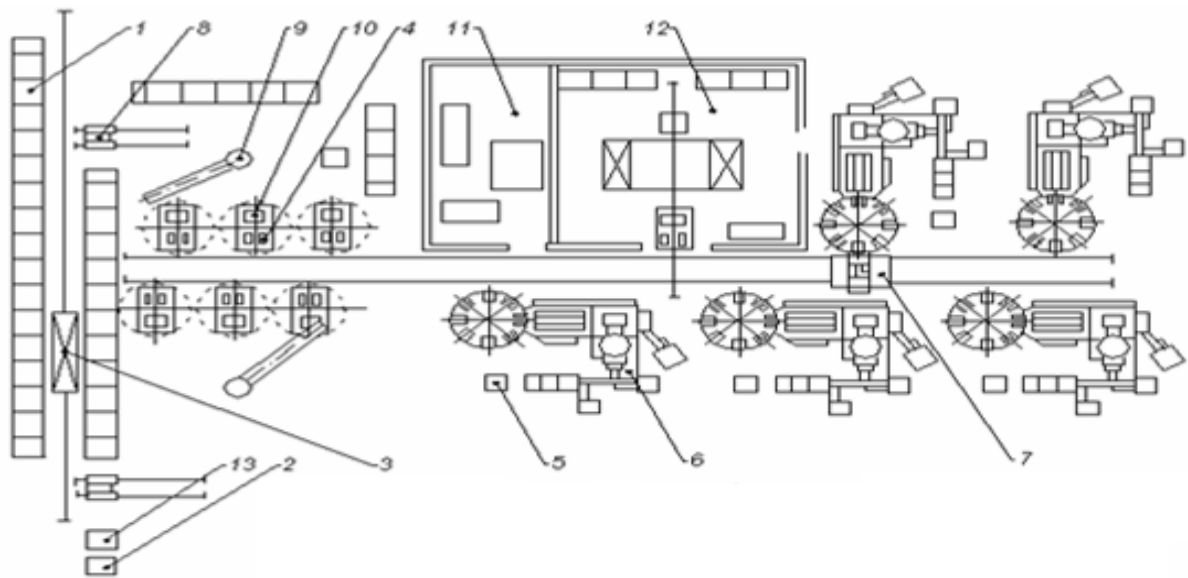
Схема ГВС виробництва корпусних деталей
